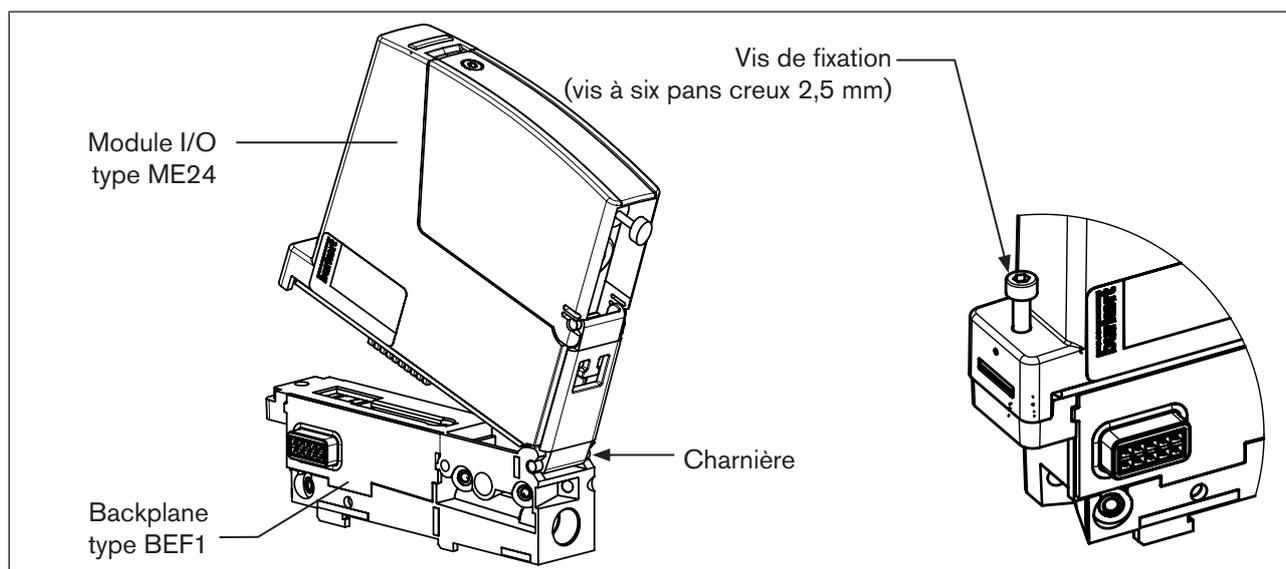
Monter le module E/S de type ME24 sur la backplane de type BEF1
